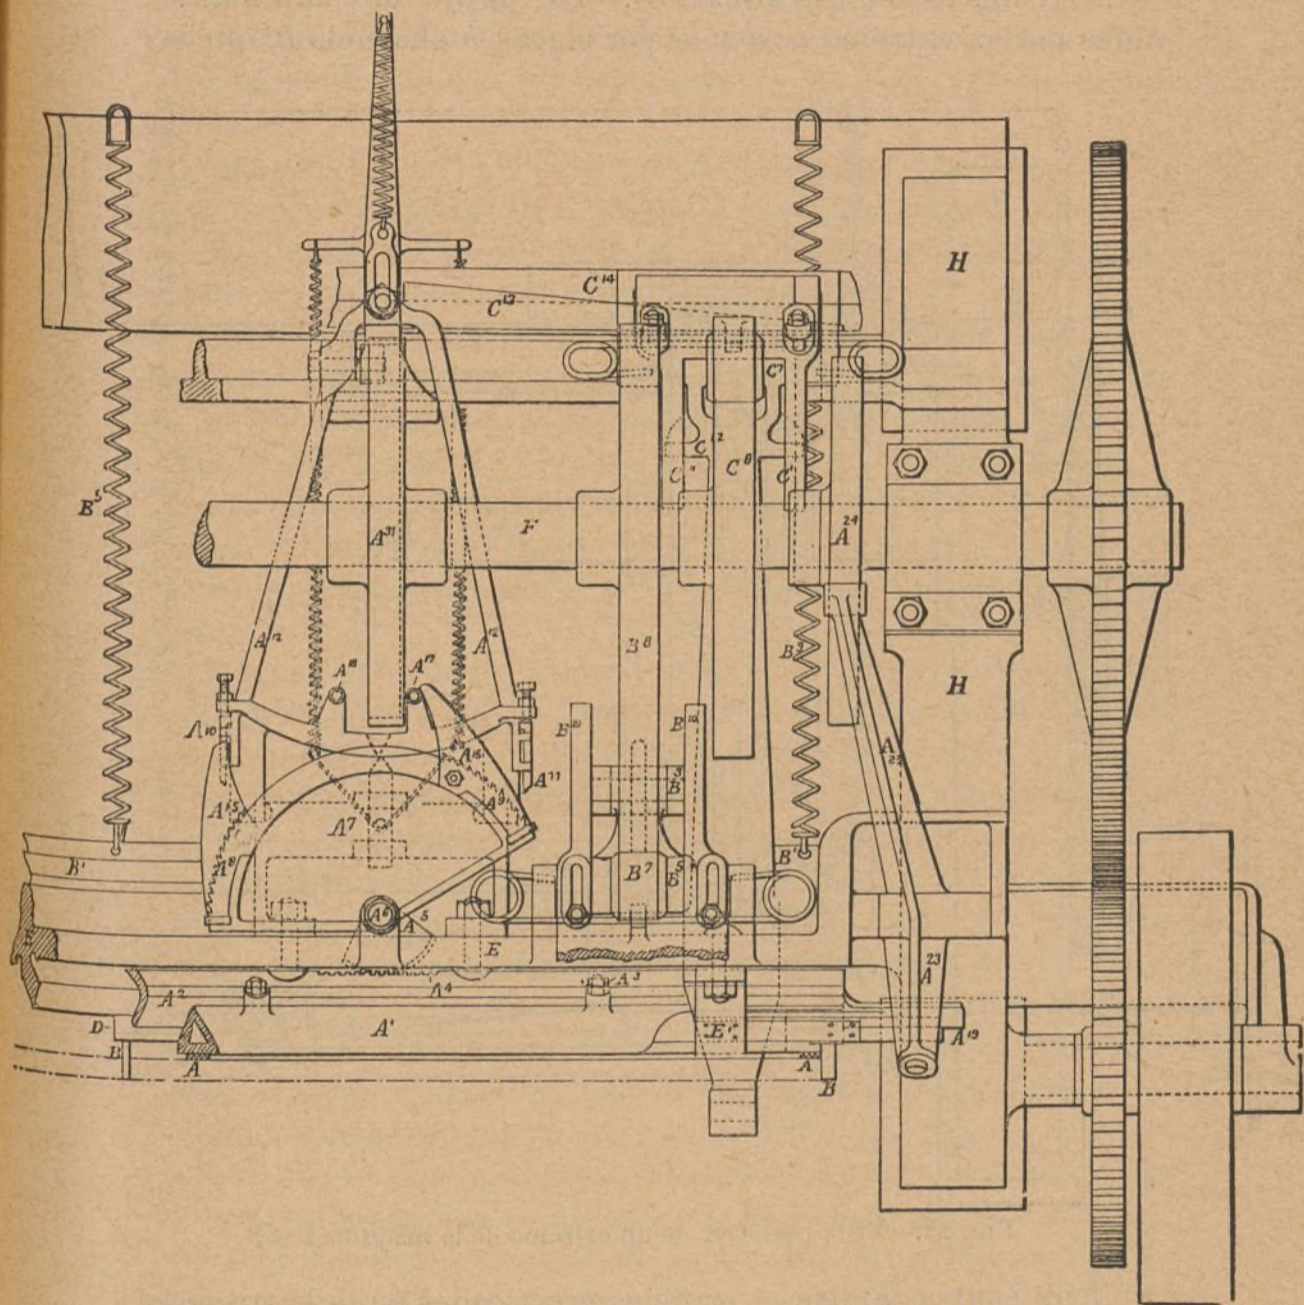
Vista anterior de un extremo de la máquina Paget.
